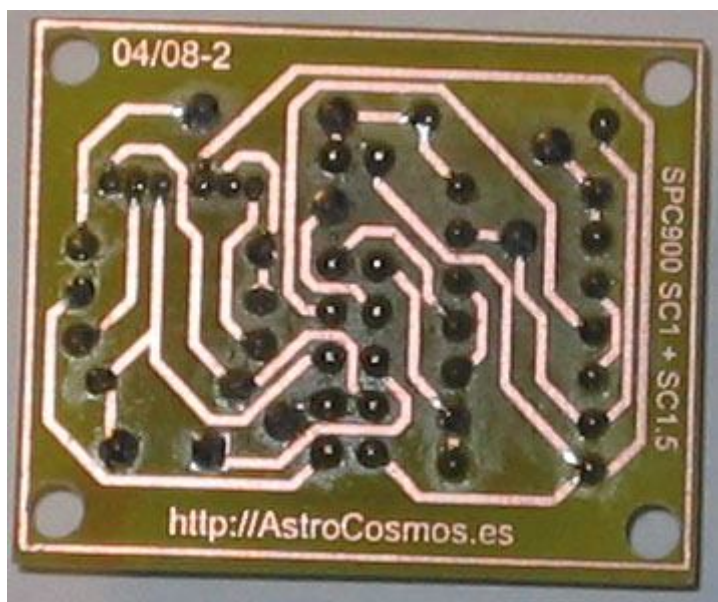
Fotografía del circuito por la cara de pistas y soldaduras
